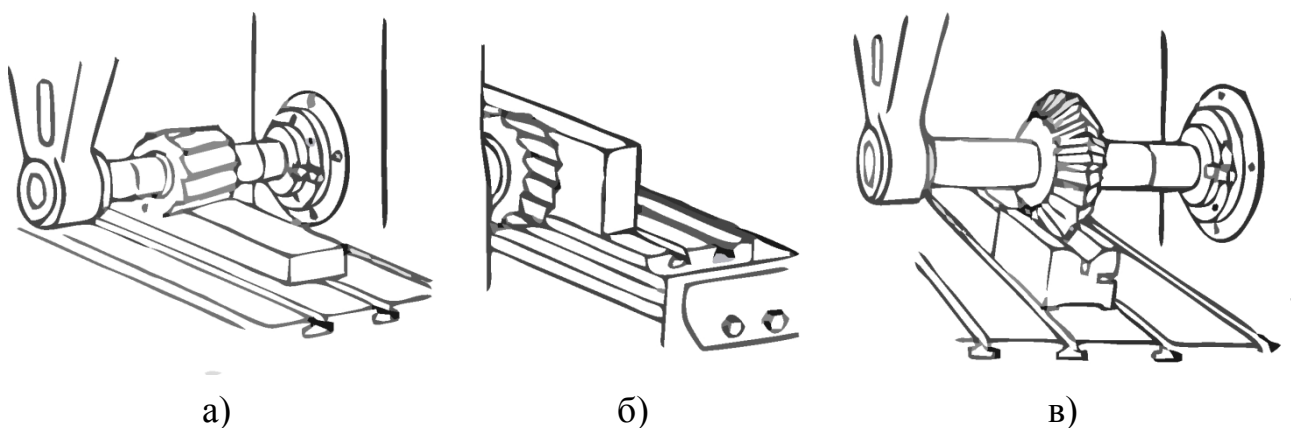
Фрезерування площин: а –циліндричною фрезею, б –торцевою фрезею, в –кутовою фрезею
